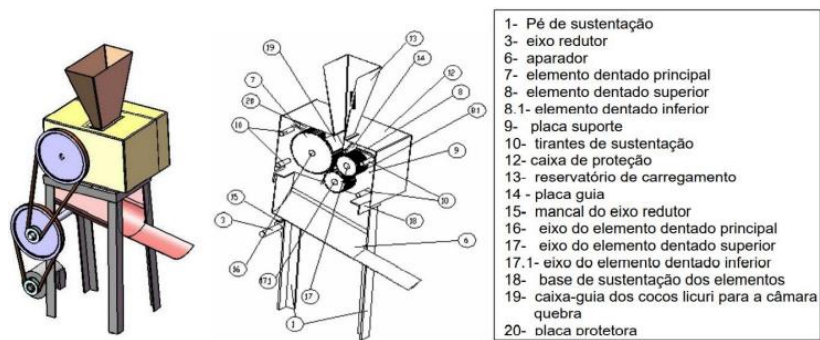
Modelo CAD 3D do conjunto do protótipo beta (Silva 2008)
